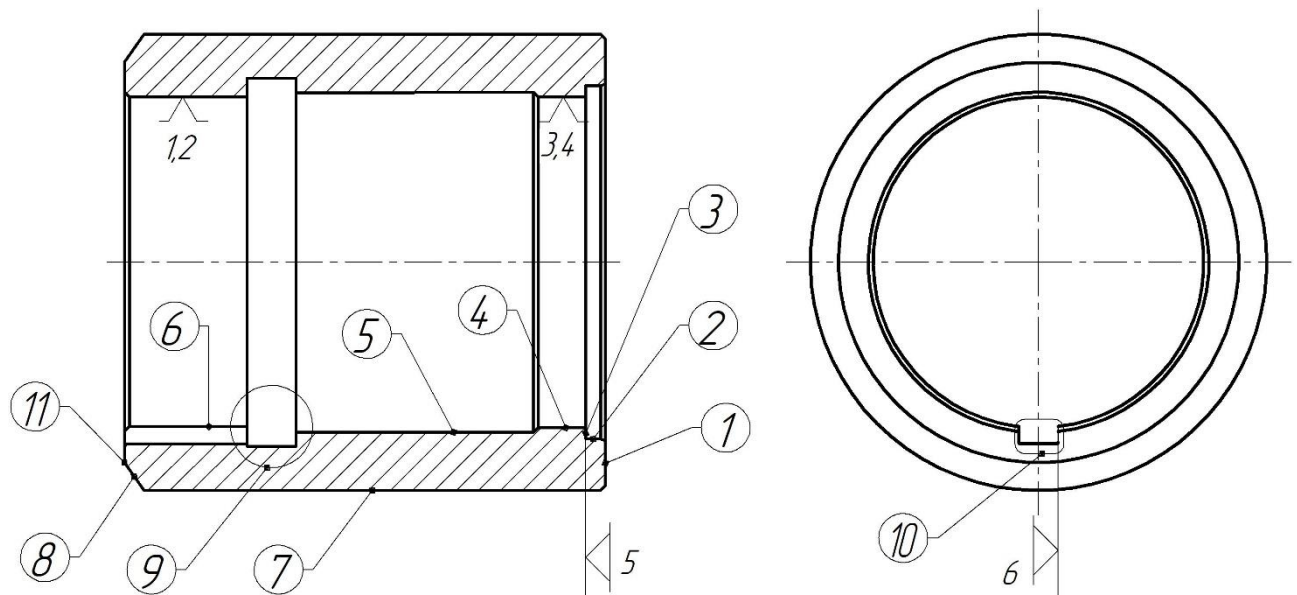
Ескіз деталі «Барабан» із нумерованими поверхнями
